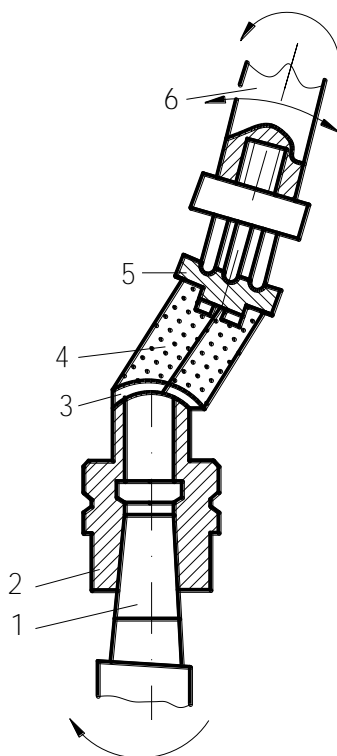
Схема полирования выпуклой поверхности заготовки линзы
